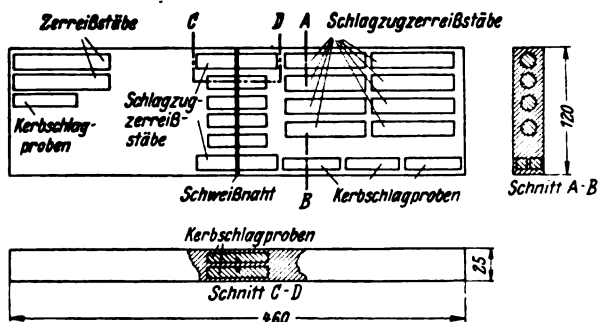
Entnahme der Proben aus den Schweißverbindungen.
